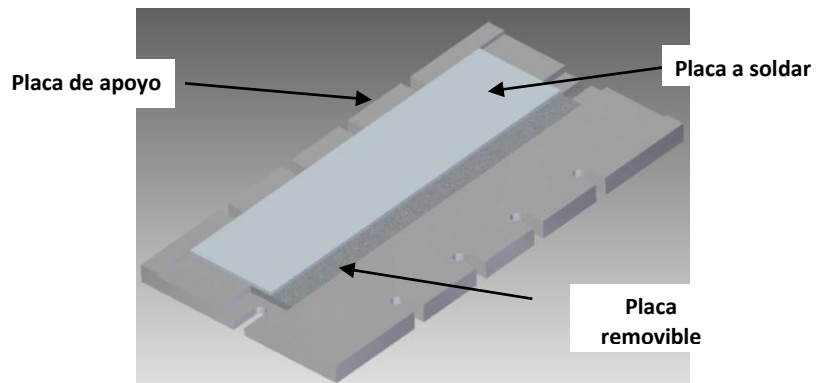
Ensamble de la placa removible sobre la placa de apoyo; placas a soldar. Fuente propia.
